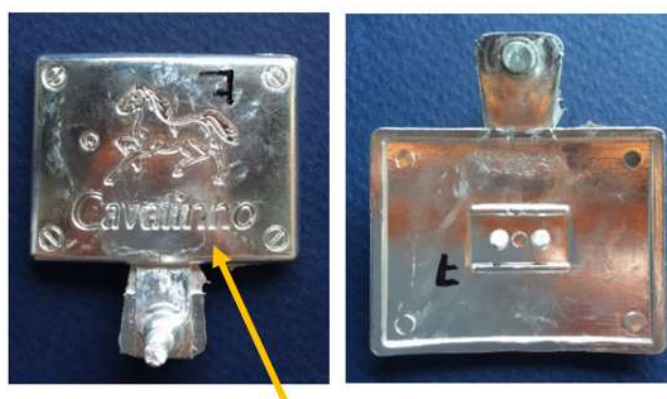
Ensaio B7 - MZ5P03TE6TA005TS2MS – Peça com fissura central assinalada e fissuras na zona das letras
